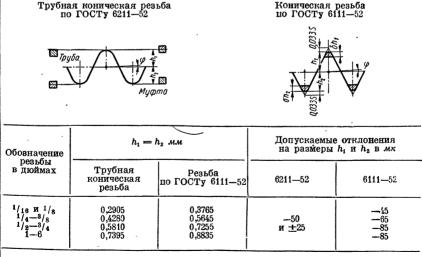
Расположение полей допусков на высоту профиля замковой резьбы
